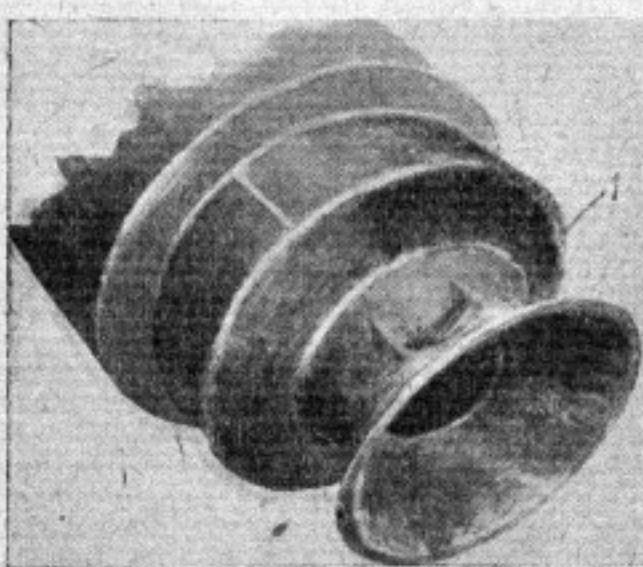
Топливник ЗИС-13; 1 — трещина нижнего сварочного шва
